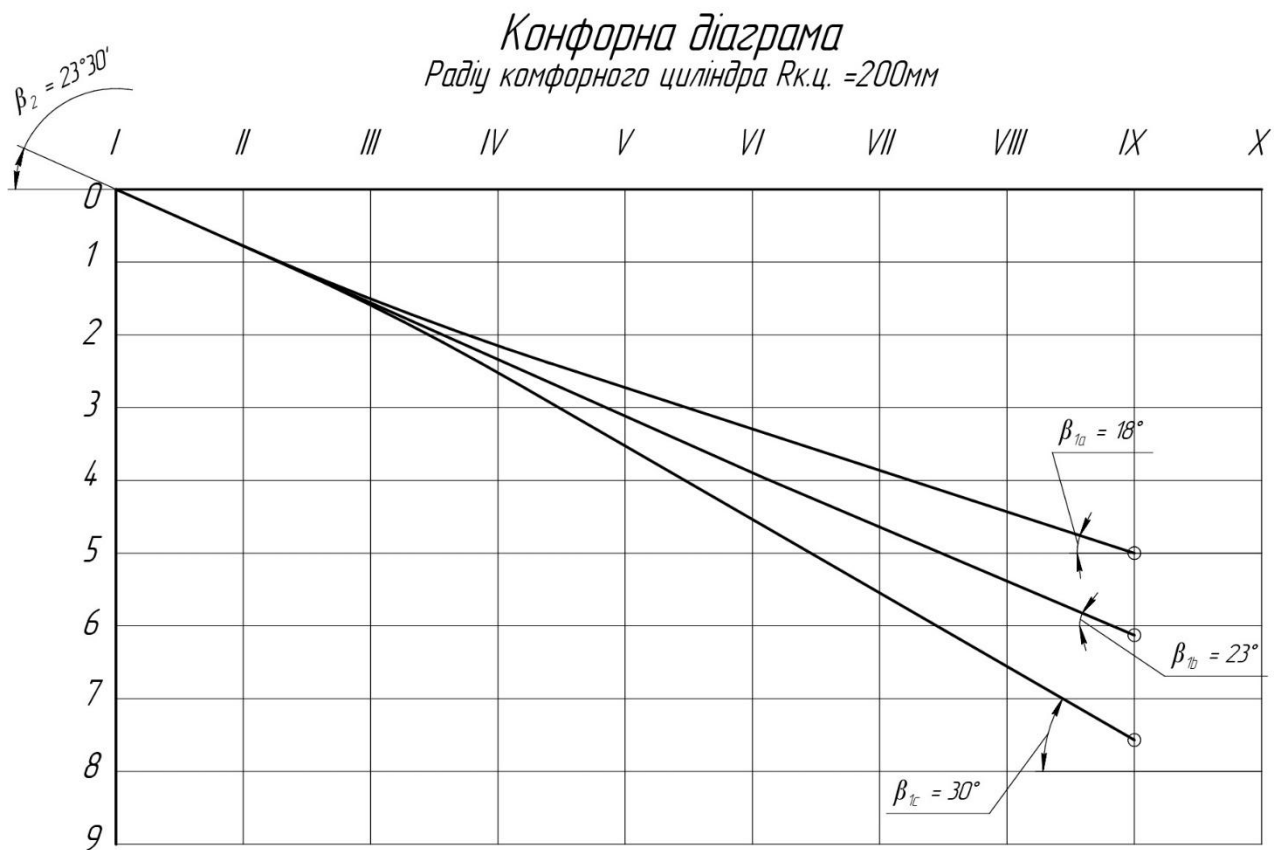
Профілювання поверхні лопаті на розгортці циліндра
